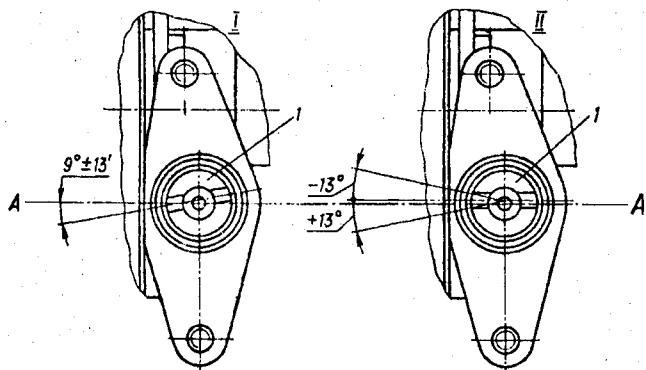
Установка ведомой шестерни привода датчика-распределителя: I – меньший сектор поводка шестерни привода; II – положение паза до установки шестерни; III – положение паза после установки шестерни; А – А – продольная ось двигателя
